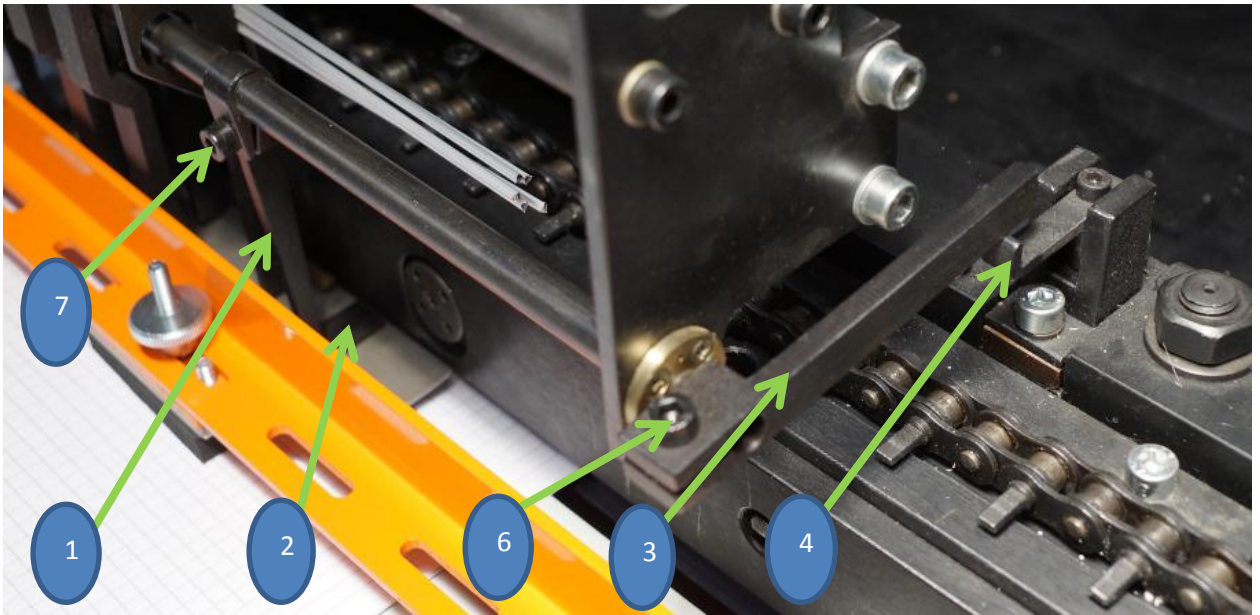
1 –толкатель ригеля; 2 – язычок толкателя ригеля; 3 – рычаг толкателя ригеля; 4 – язычок приводного устройства; 6 - винт крепления рычага толкателя; 7-крепление толкателя
